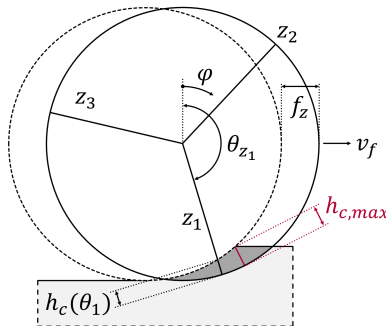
Eingriffsbedingungen zwischen Werkzeug und Werkstück
